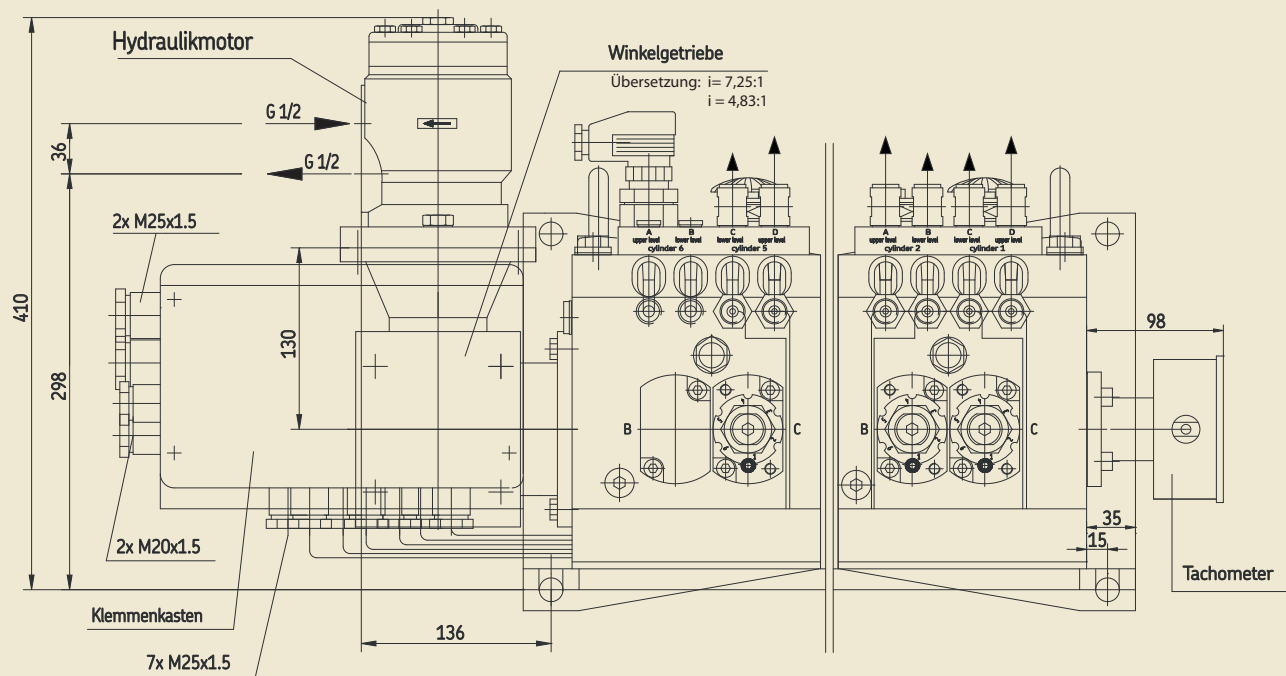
Montagezeichnung PC Ölschmierpumpenaggregat mit Hydraulikmotor, Seitenansicht
